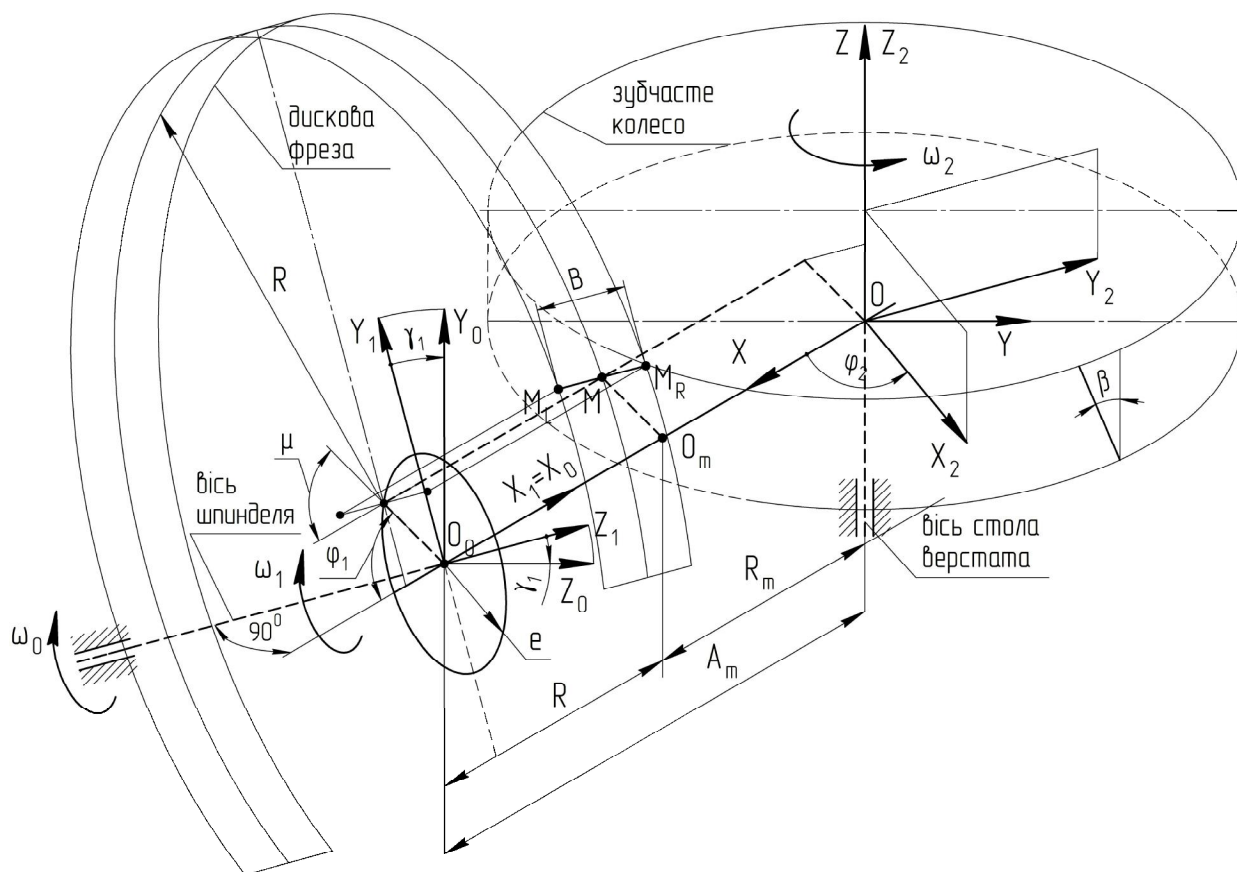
Формоутворення дисковою фрезею профілю зубців циліндричного зубчастого колеса
